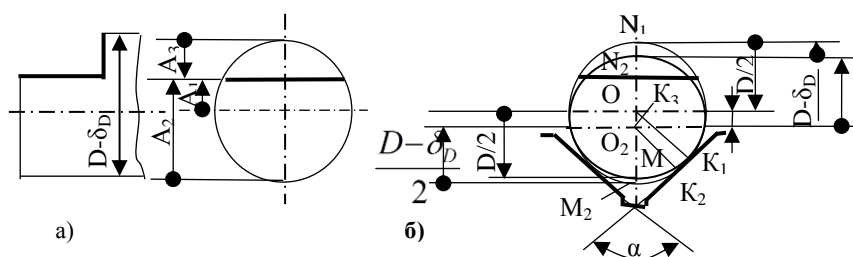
Схемы к определению погрешности установки цилиндрической заготовки на призме при различных схемах простановки операционного размера
